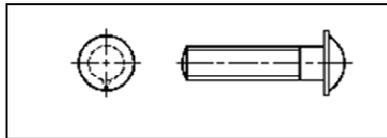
Tornillos de cabeza taladrada y de cabeza de arandela
